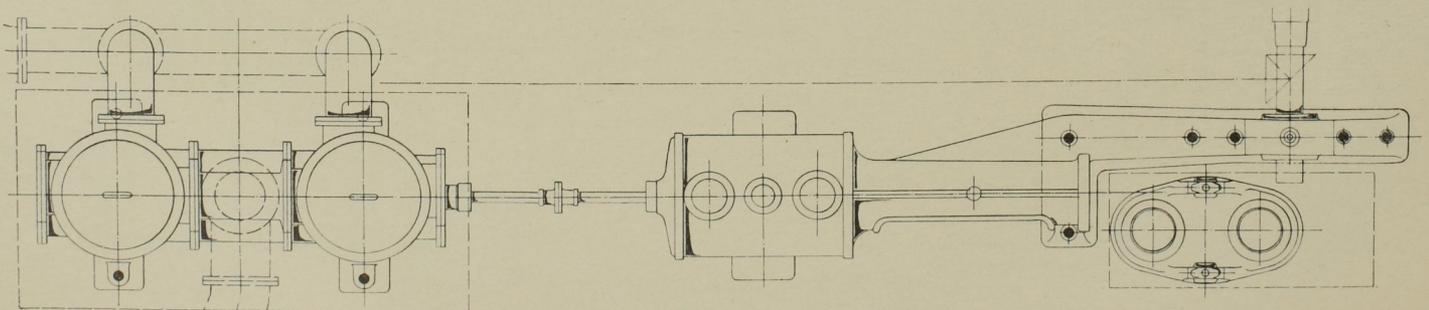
Grundriss der Pumpmaschine. Masst. 1:50.
